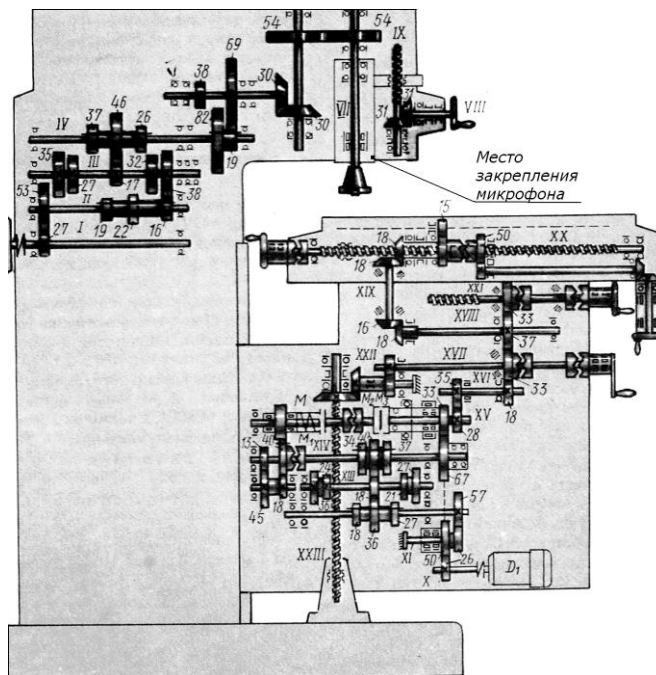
Кинематическая схема фрезерного станка 6P13 с указанием места закрепления микрофона
